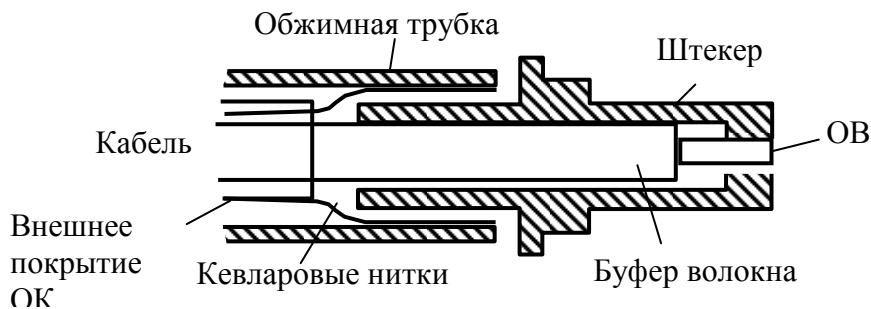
Разрез конструкции соединителя, в котором усиливающие элементы из кевлара обжаты с помощью трубки
